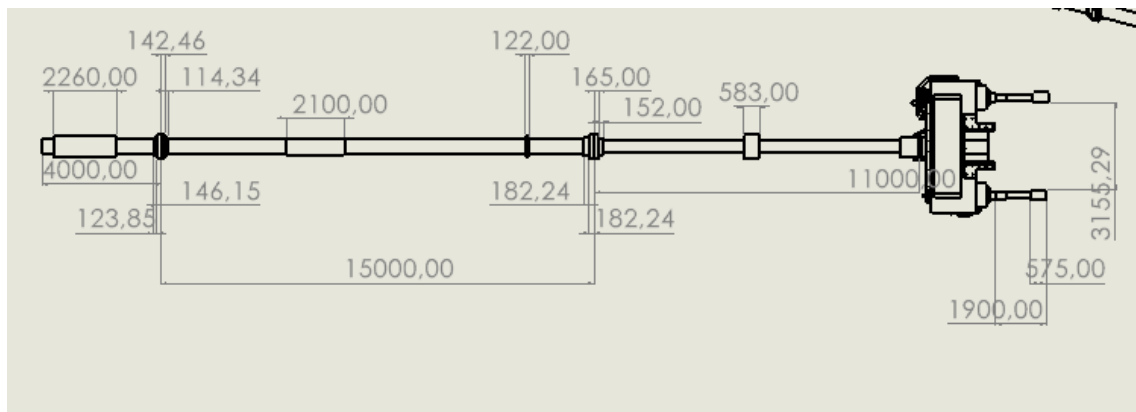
Plano alzado de la colocación de los apoyos. Fuente: Propia
